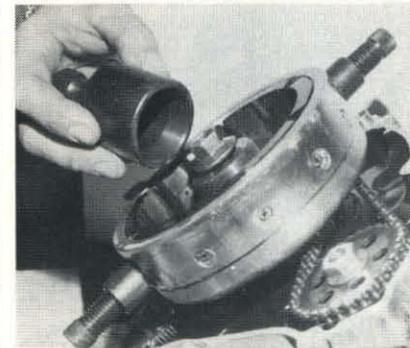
Installation de l'extracteur de rotor (Photo RMT)
